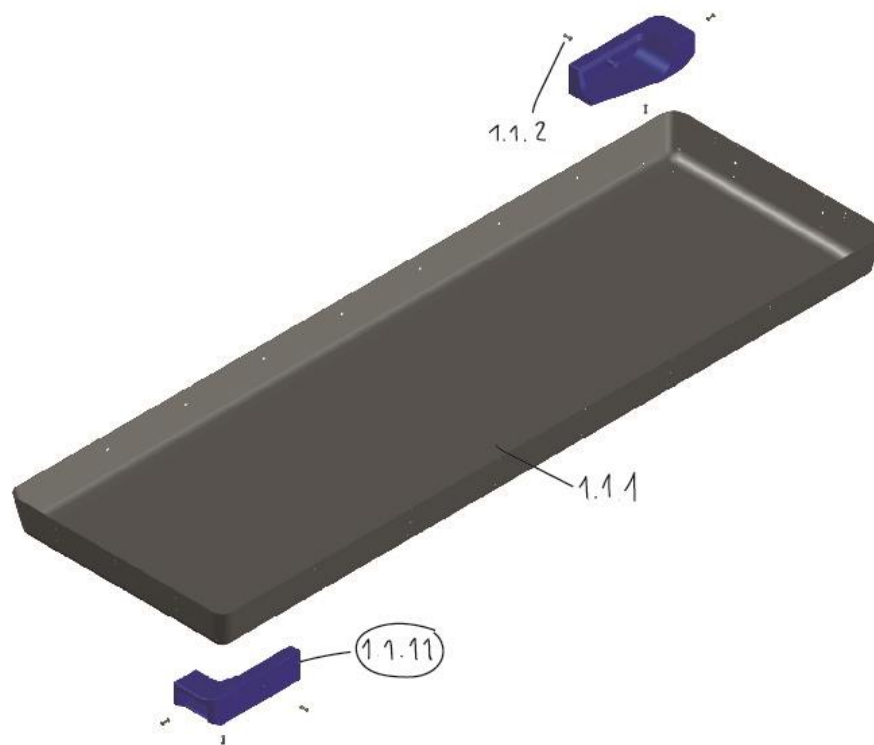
Explosionado de relaciones pieza 1.1.11
